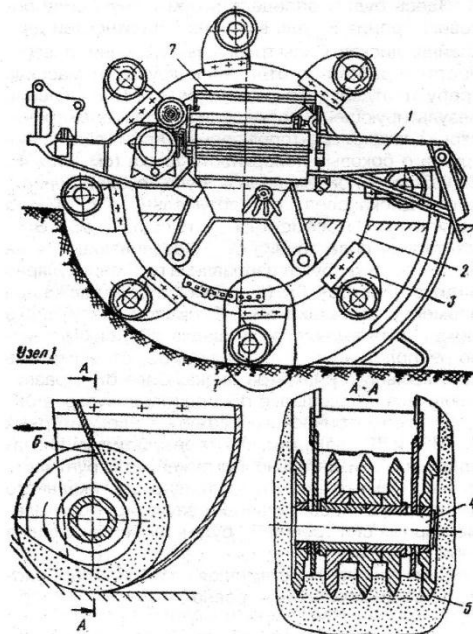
Конструкция рабочего органа роторного экскаватора
